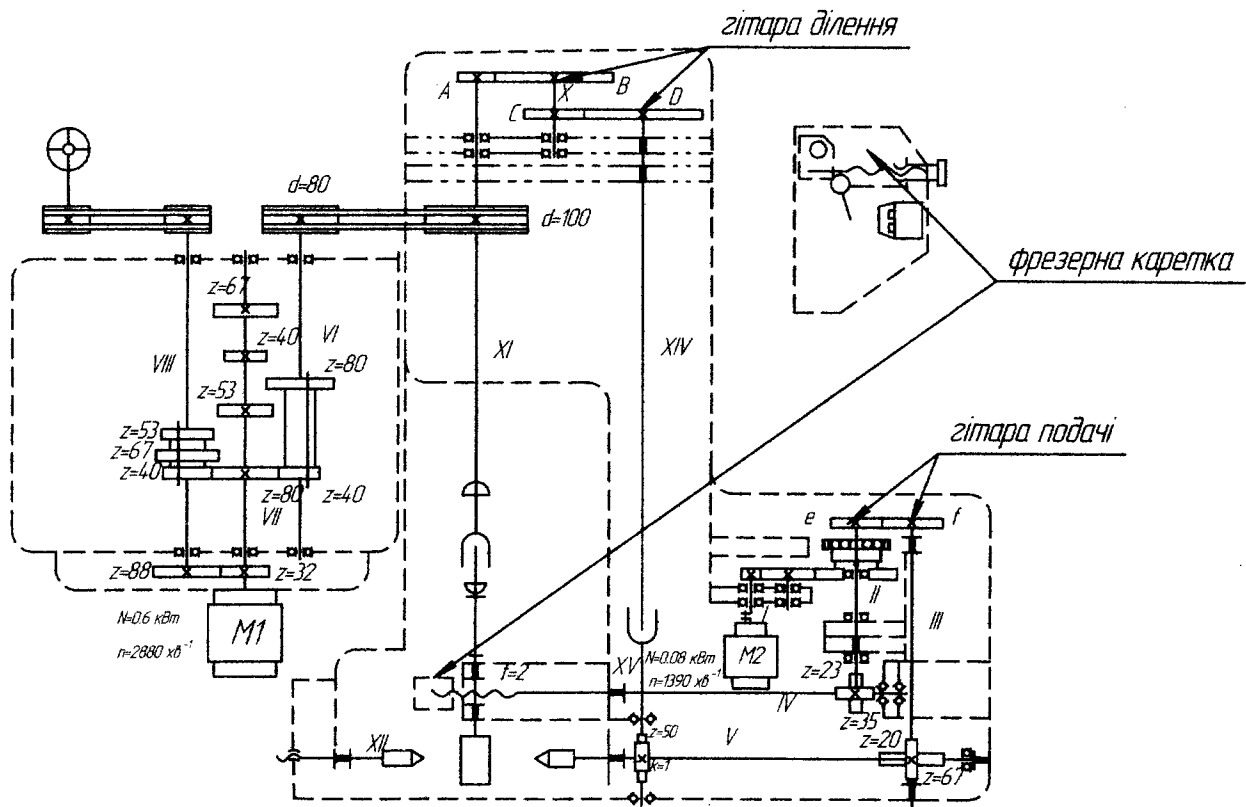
Кінематична схема зубофрезерного верстата 5А308П
